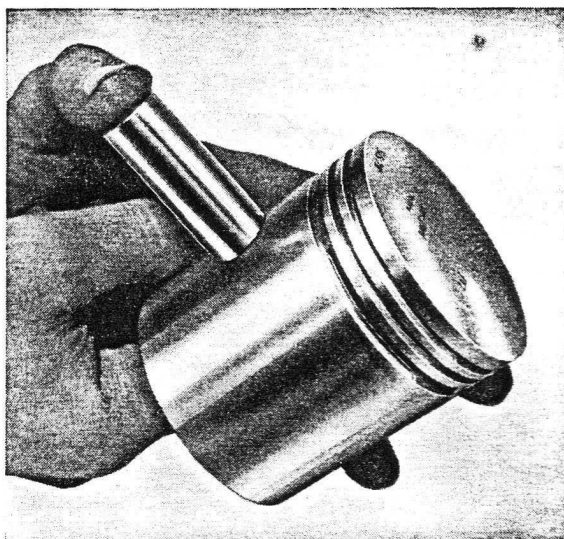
Prüfen der Passung eines Kolbenbolzens
